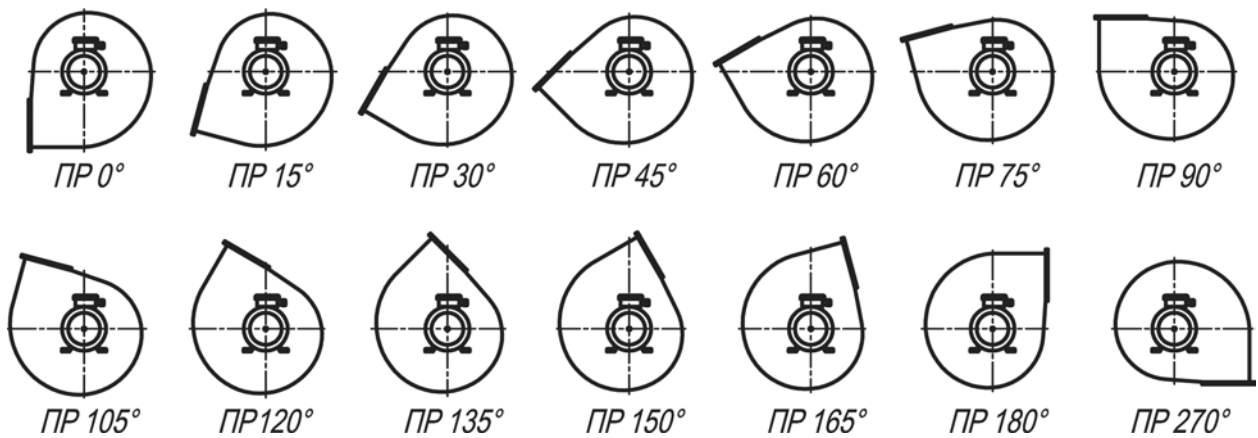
Положение корпуса тягодутьевых машин типа ВДН и ДН (ПР).
